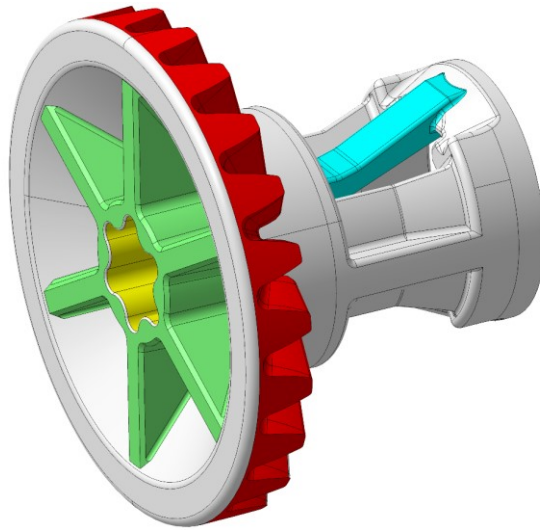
Konstrukční vývoj velkého ozubeného kola – varianta 1
